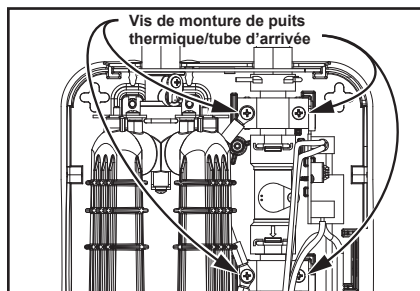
Vis de montage de puits thermique/tube d'arrivée.
